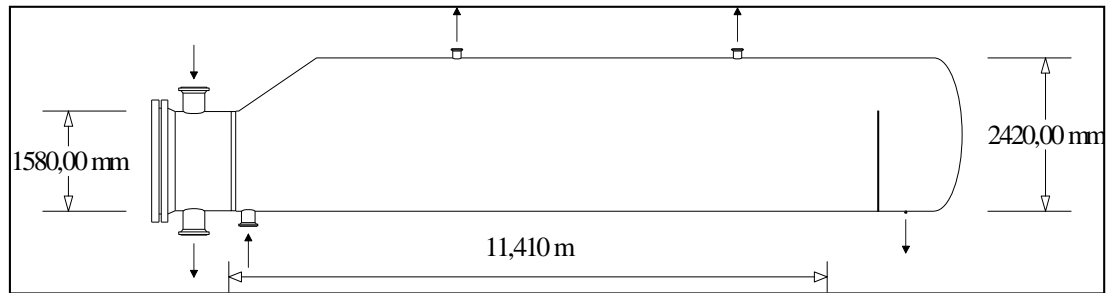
Dimensiones generales Kettle. Fuente: HTRI Output drawing.
